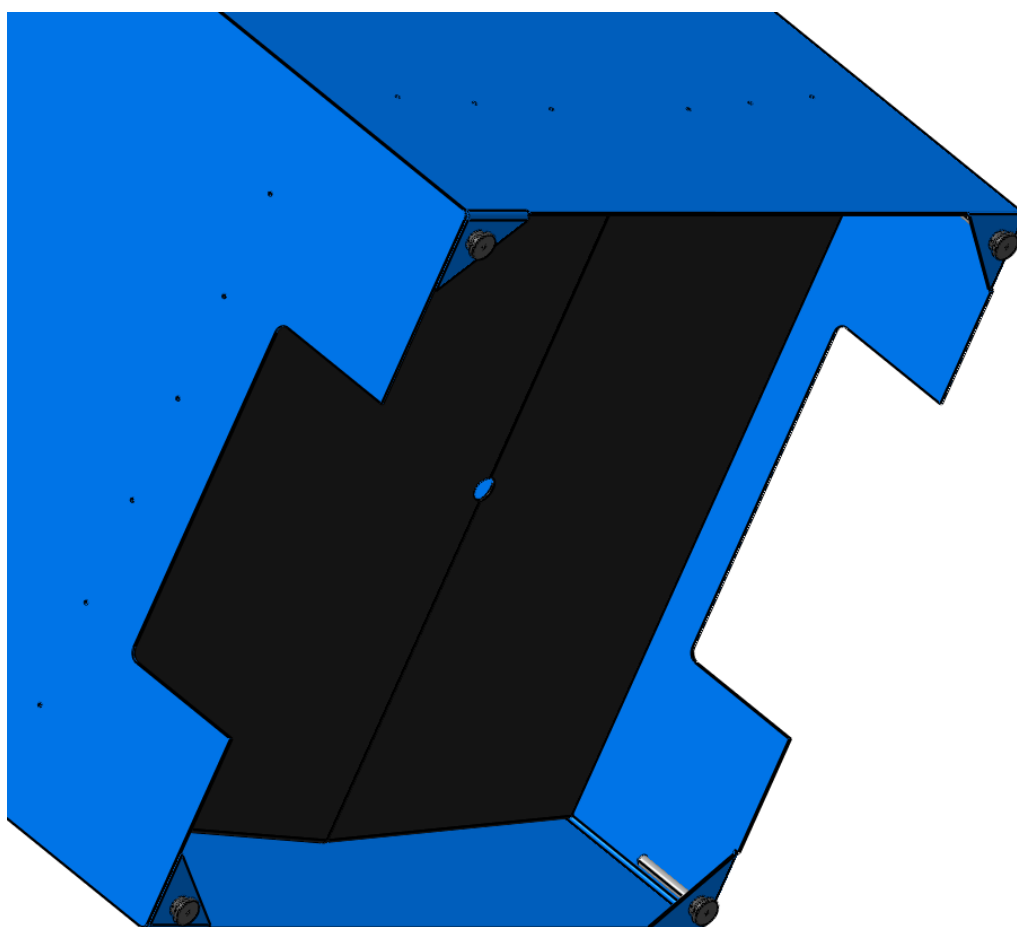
Ventilátor Alteko RFE 355 upnutý pevnou přírubou k filtračnímu zařízení
